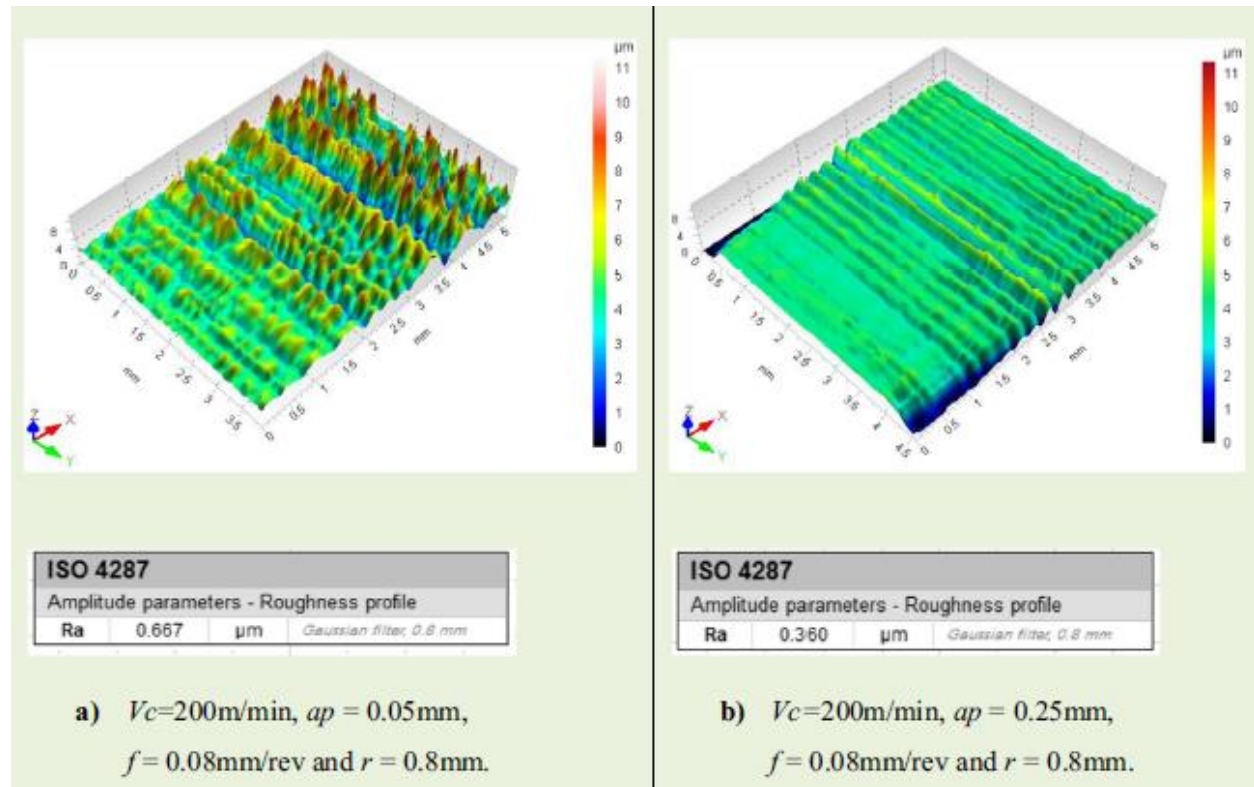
Topographie des surfaces usinées pour deux régimes de coupe.
